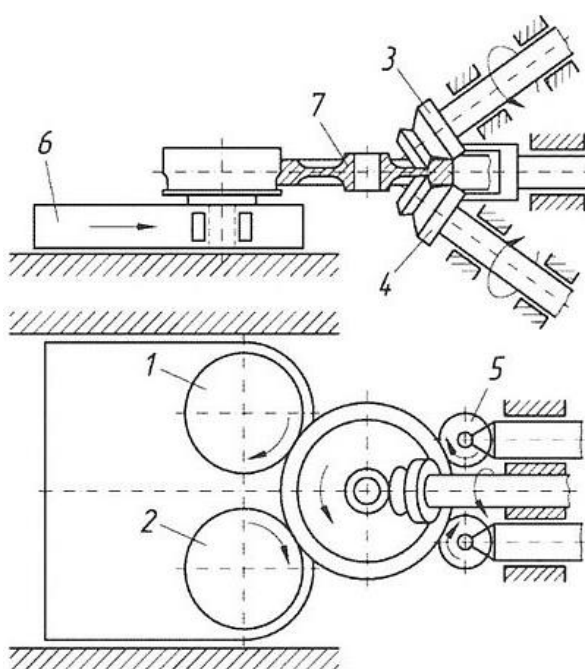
Схема прокатки на колесопрокатном стане горизонтального типа: 1,2 – коренные рабочие валки; 3,4 – наклонные рабочие валки; 5 – ролики; 6 – каретка; 7 – заготовка колеса [3]
